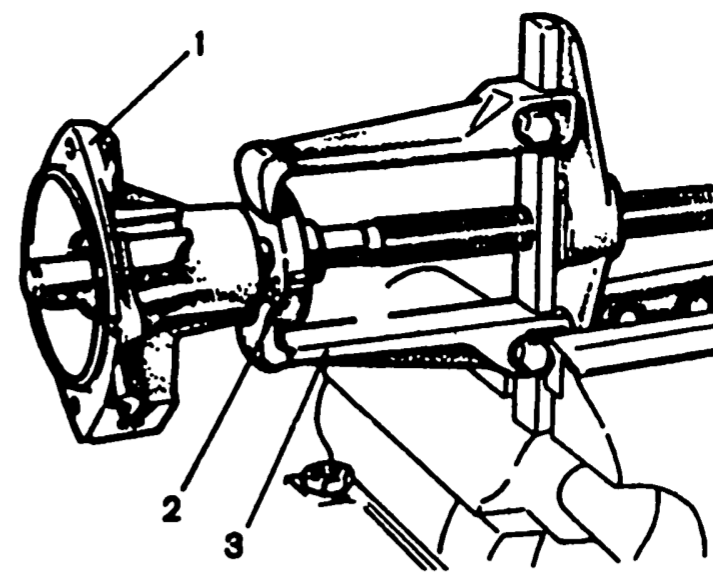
Снятие ступицы шкива: 1 - крышка корпуса насоса; 2 - ступица шкива; 3 - съемник
